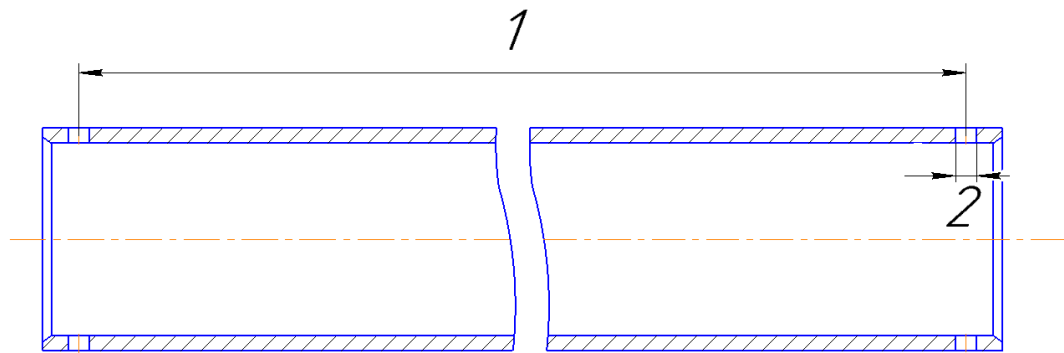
Креслення оброблюваної деталі з необхідними розмірами
